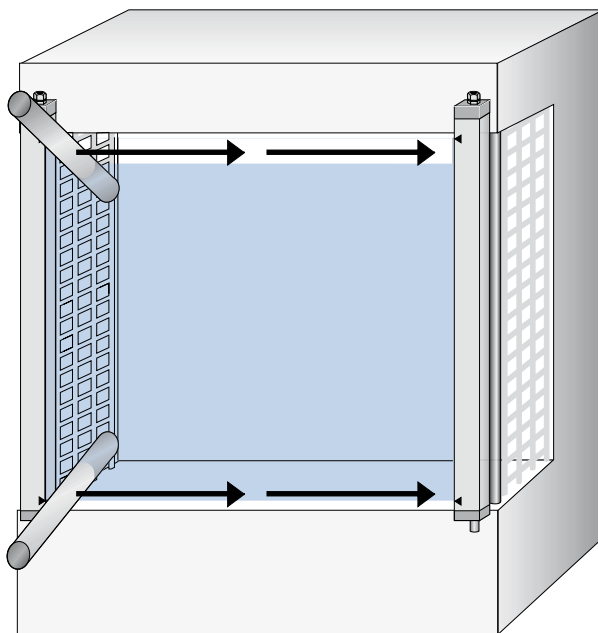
Verifica giornaliera del dispositivo di protezione: secondo passo
